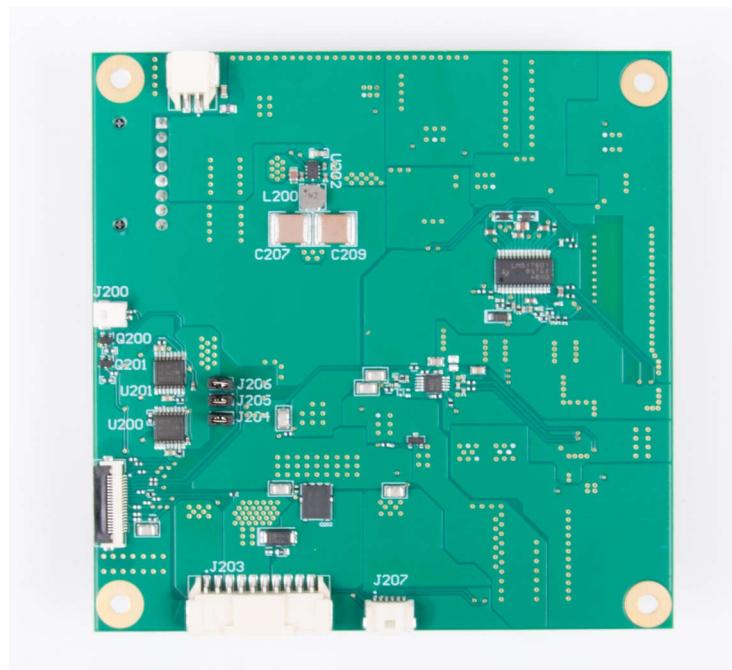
DLP5532PROJHBQ1EVM 照明驱动器 PCB (底部)
